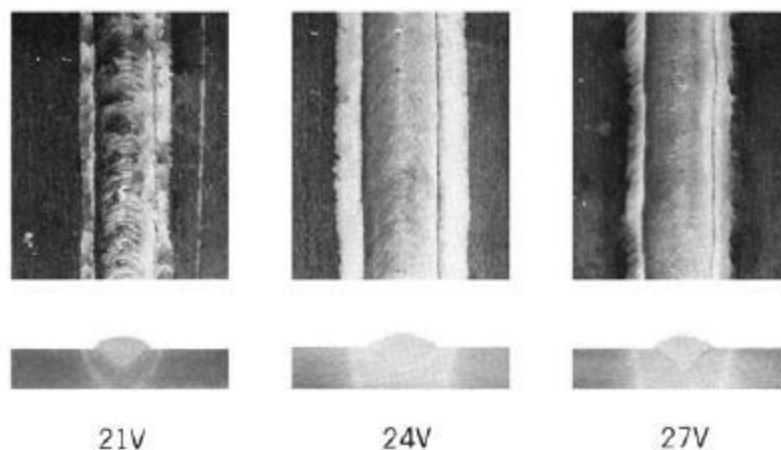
Efeito da tensão de soldadura na penetração da solda [25]
